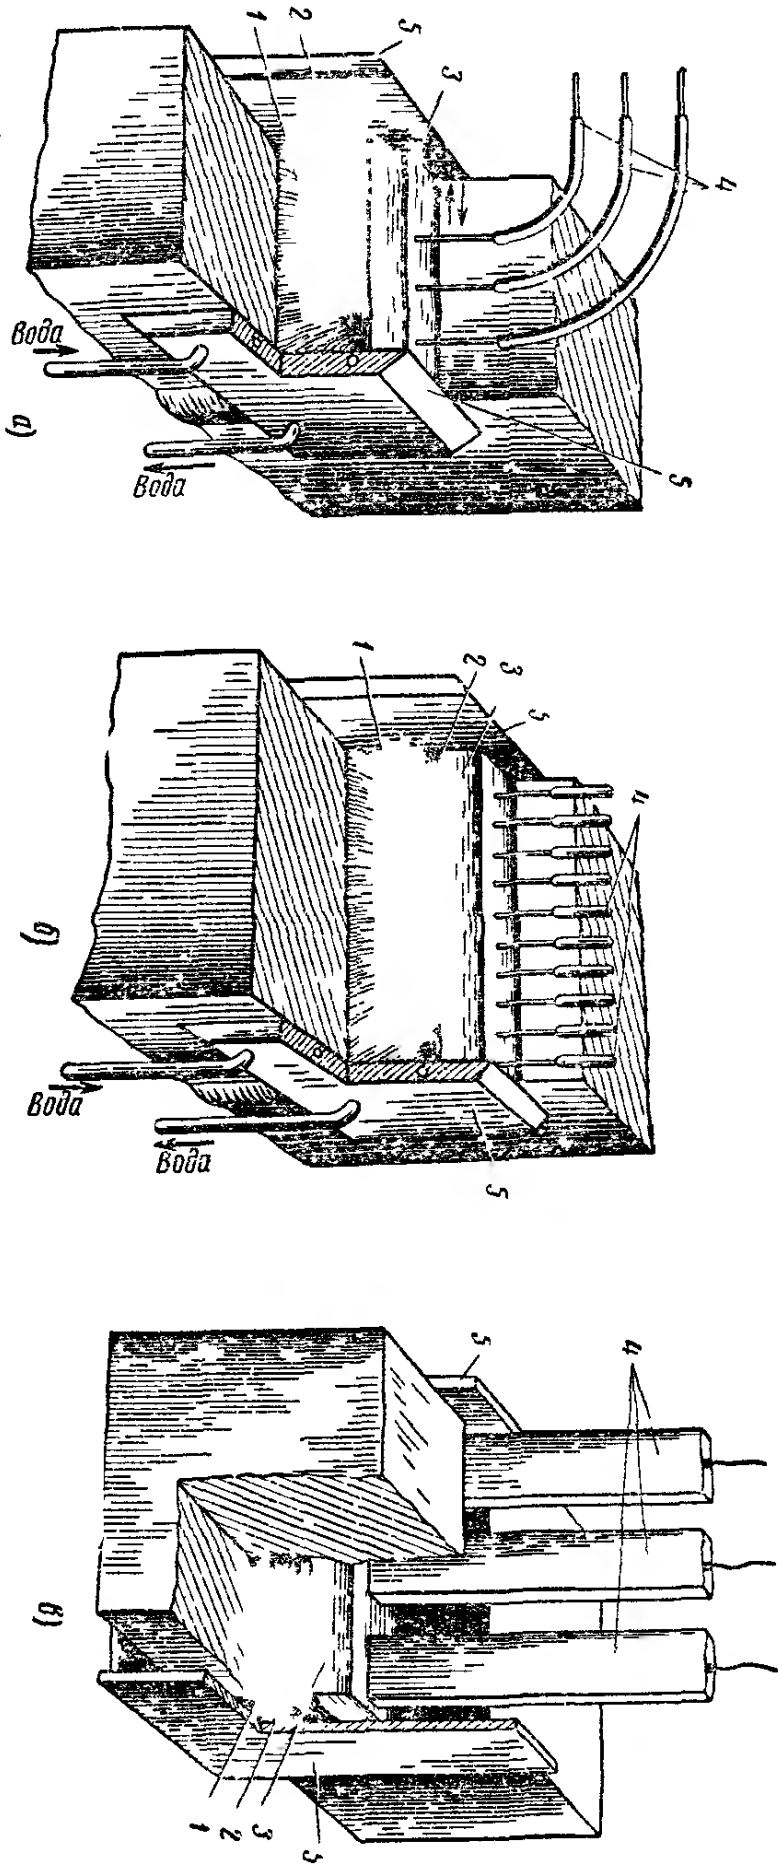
Способы многоэлектродной электрошлаковой сварки:
